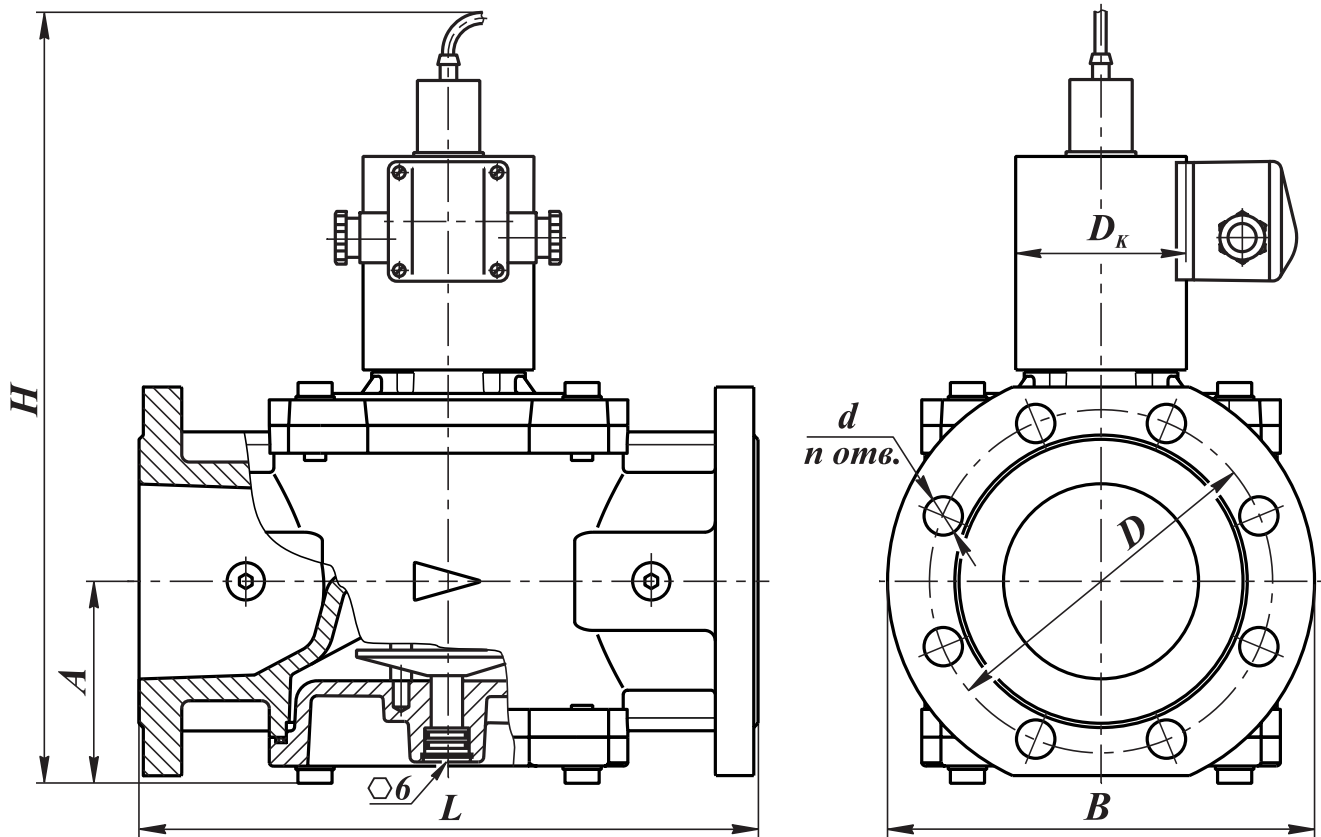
Клапаны на DN 65 - 100 фланцевые с ручным регулятором расхода и датчиком положения (исполнение: с присоединительными фланцами PN 16)
